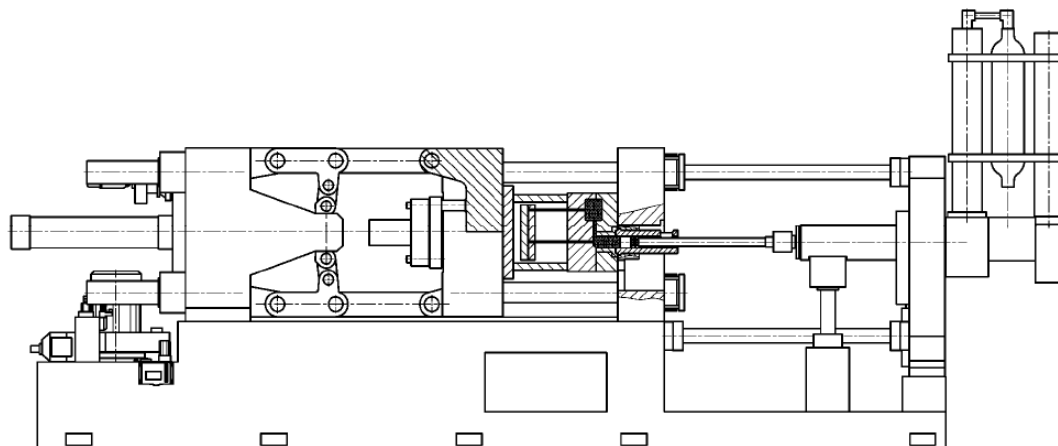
Máquina de fundição injetada de câmara fria horizontal (configuração típica)
